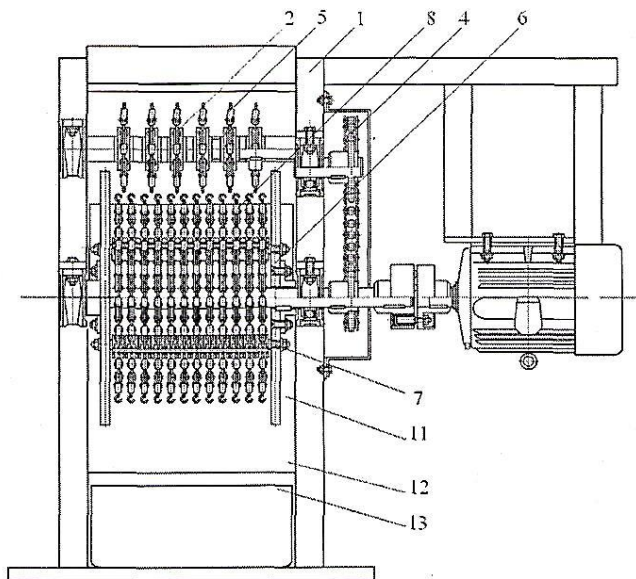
Устройство для заготовки хвойной лапки (вид спереди)
